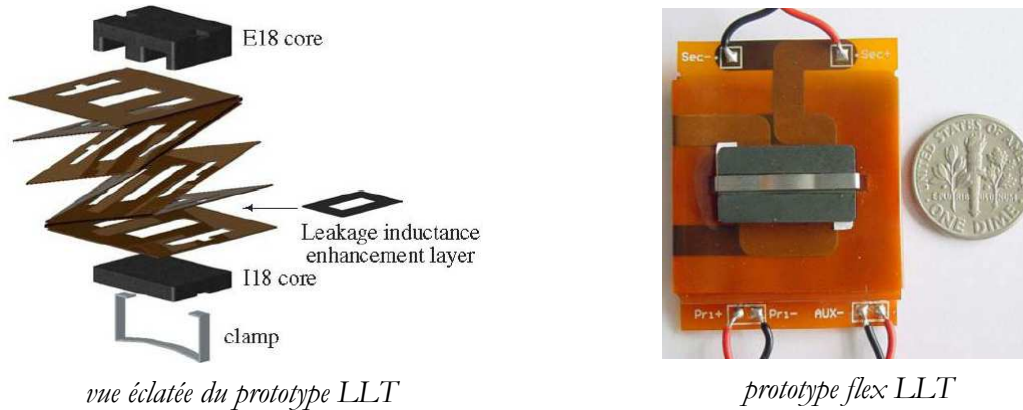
Prototype LLT flex PCB (Ferreira)
